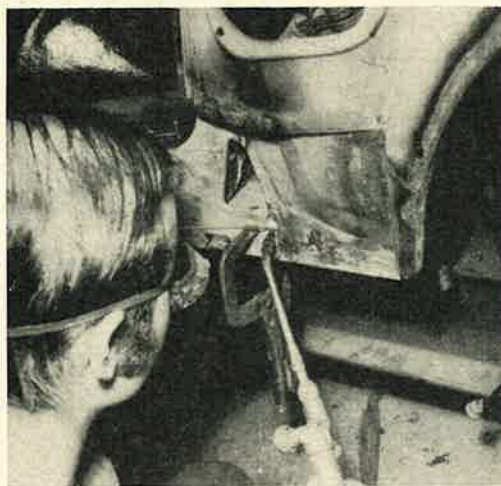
Soudage oxyacétylénique du gousset renfort latéral gauche (photo R.T.C.).
